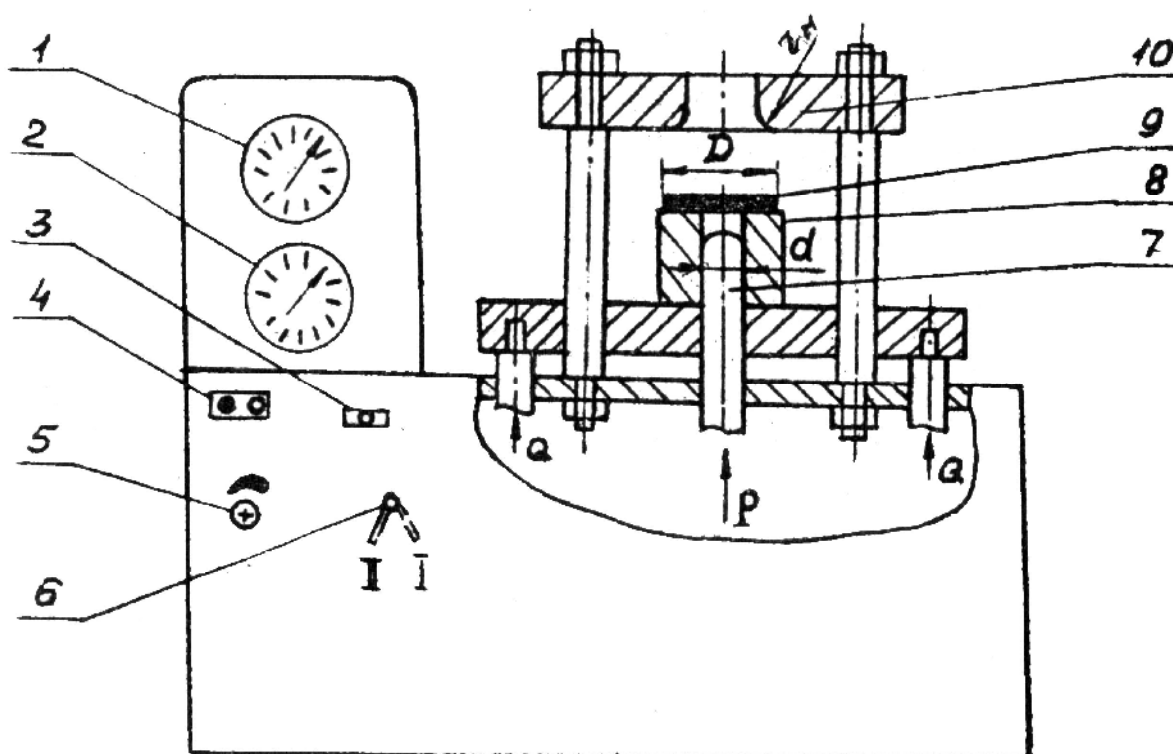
Схема испытательной машины для вытяжки колпачков:
